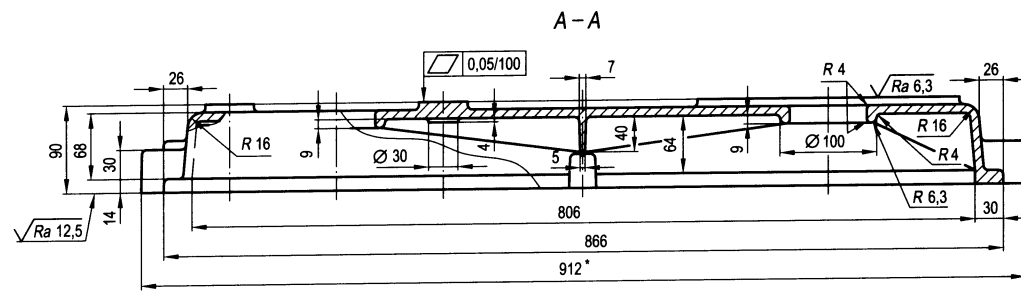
Определение размеров боковой крышки корпуса (размеры см. на листах 23.2, 23.3; $H \geq 0,08 L_K$; $l_B \leq 12 d_B$)
